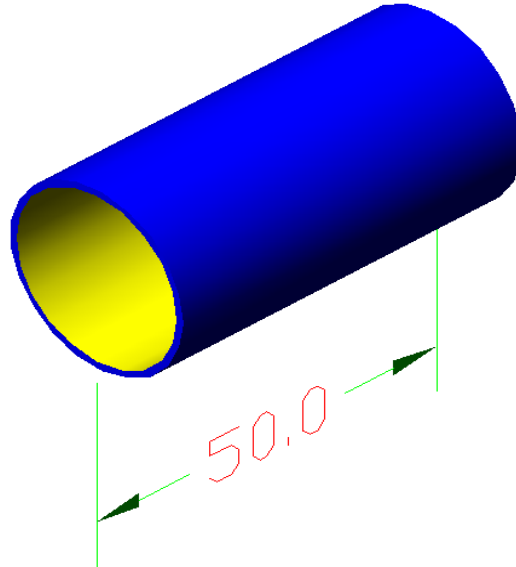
Probeta de Tubo a partir de lámina galvanizada
